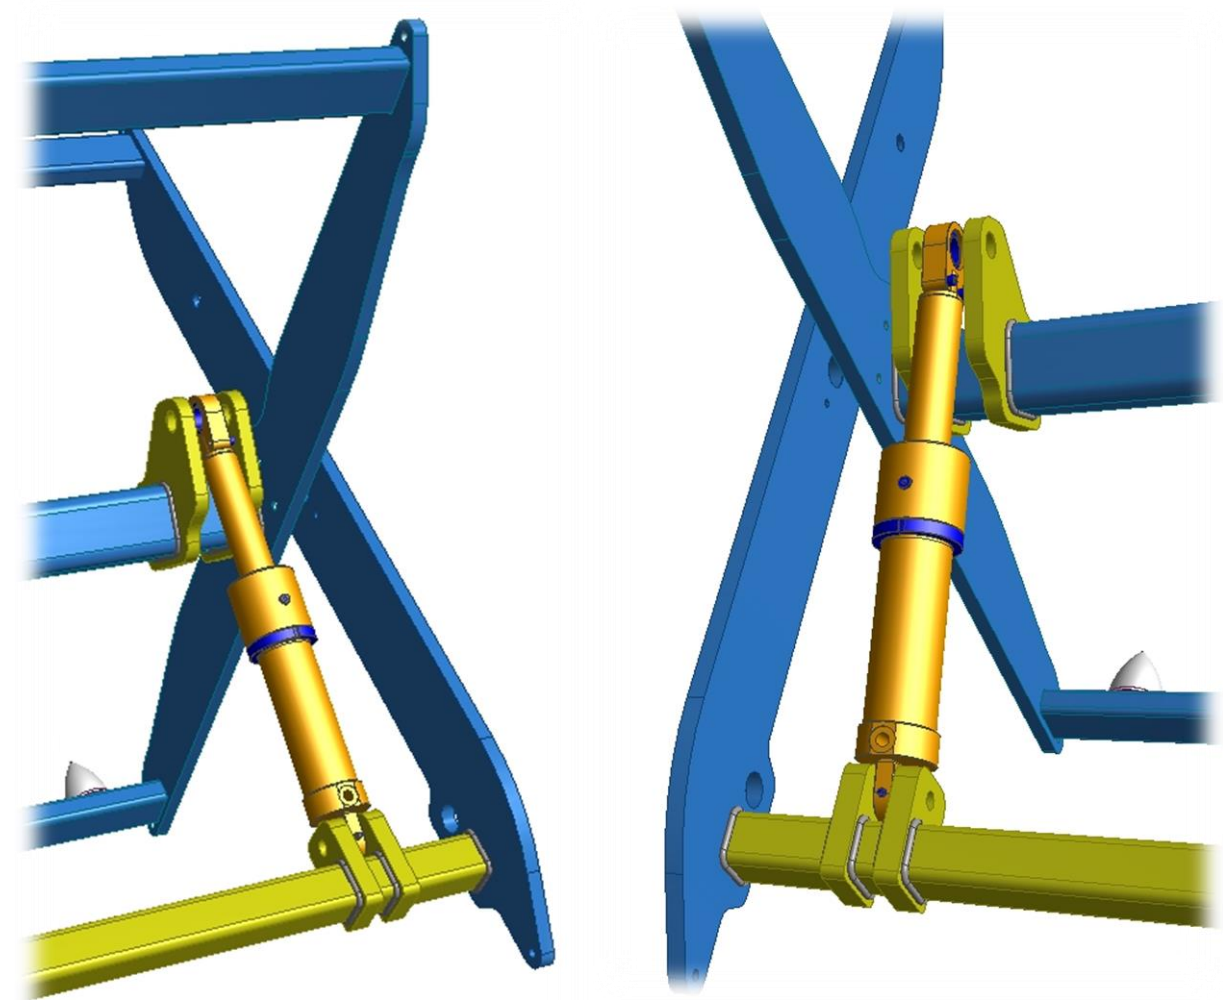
Spojení spodního a horního rámu v řezu k částem mechanismu.
